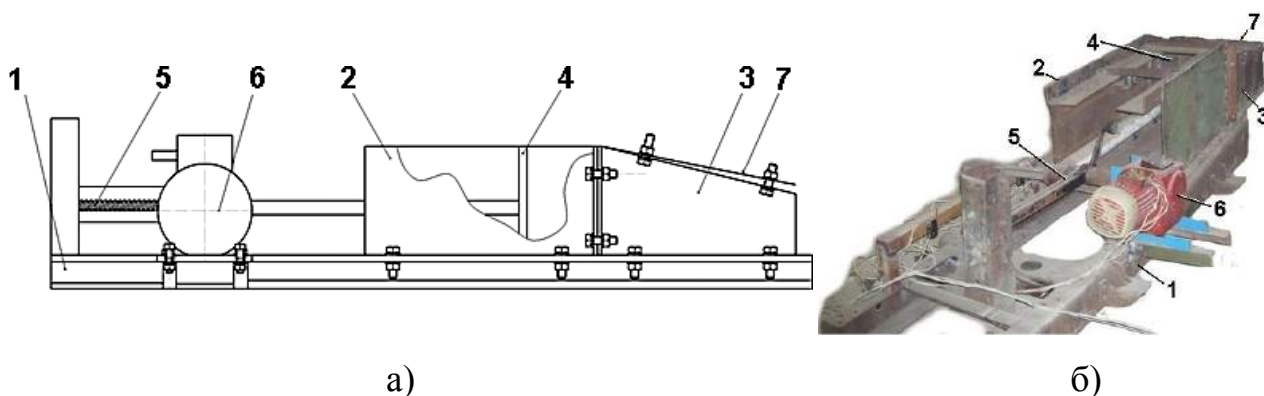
Прес попереднього ущільнення рослинної сировини: а – конструктивно–технологічна схема; б – загальний вигляд; 1 - рама; 2 – приймально–формуюча камера; 3 – пресувальна камера; 4 - ущільнюючий поршень; 5 – механізм приводу поршня; 6 - електроприводний мотор–редуктор; 7 – верхня формуюча стінка.
